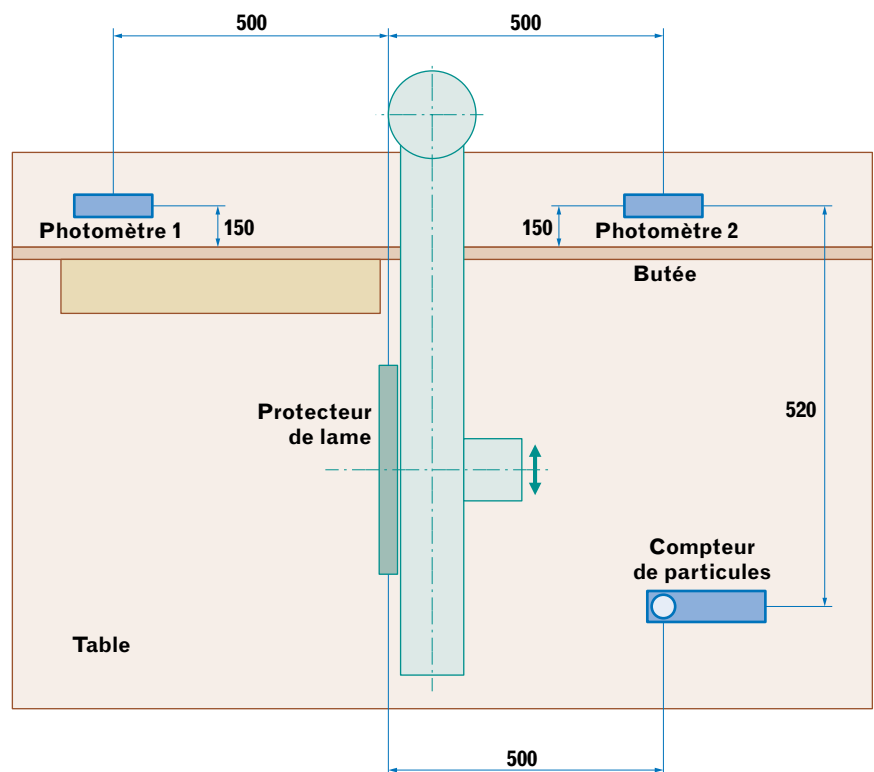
Emplacement des photomètres sur la machine - Location of the photometers on the machine
